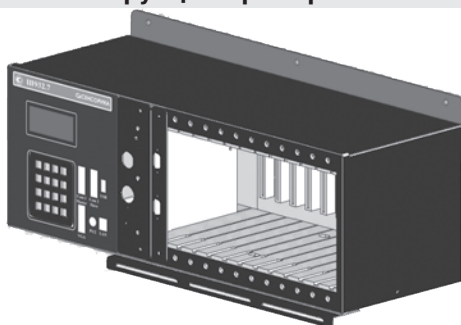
Конструкция прибора Ш932.7 исп. 2
